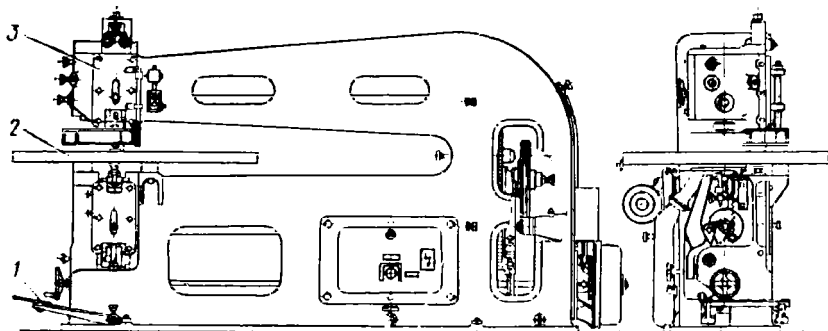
Схема шпопочно-пачечного станка ПШ-2:
